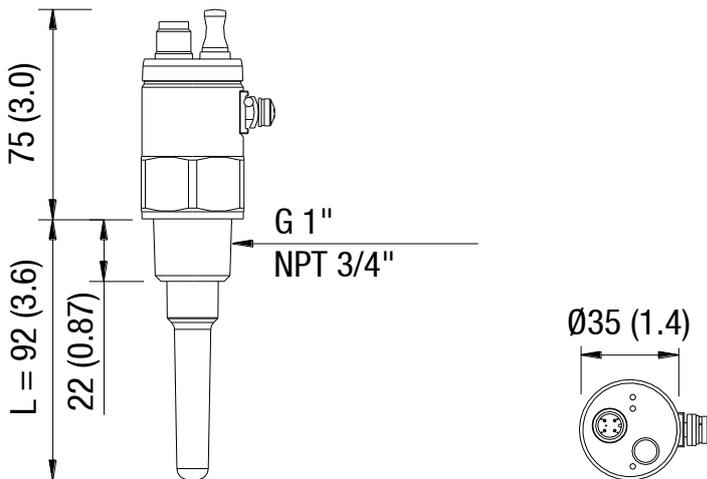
Abmessungen CN 7121, Gehäuse Ø 35 mm
